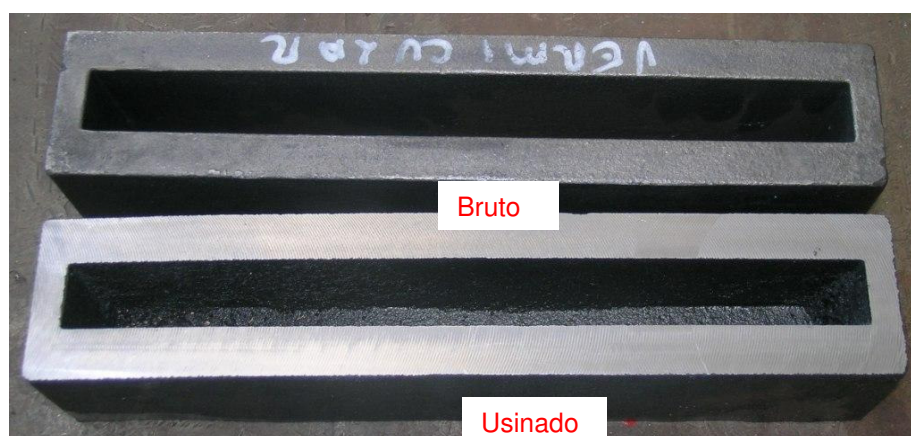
Face superior do corpo-de-prova usinada e em bruto de fundição.
